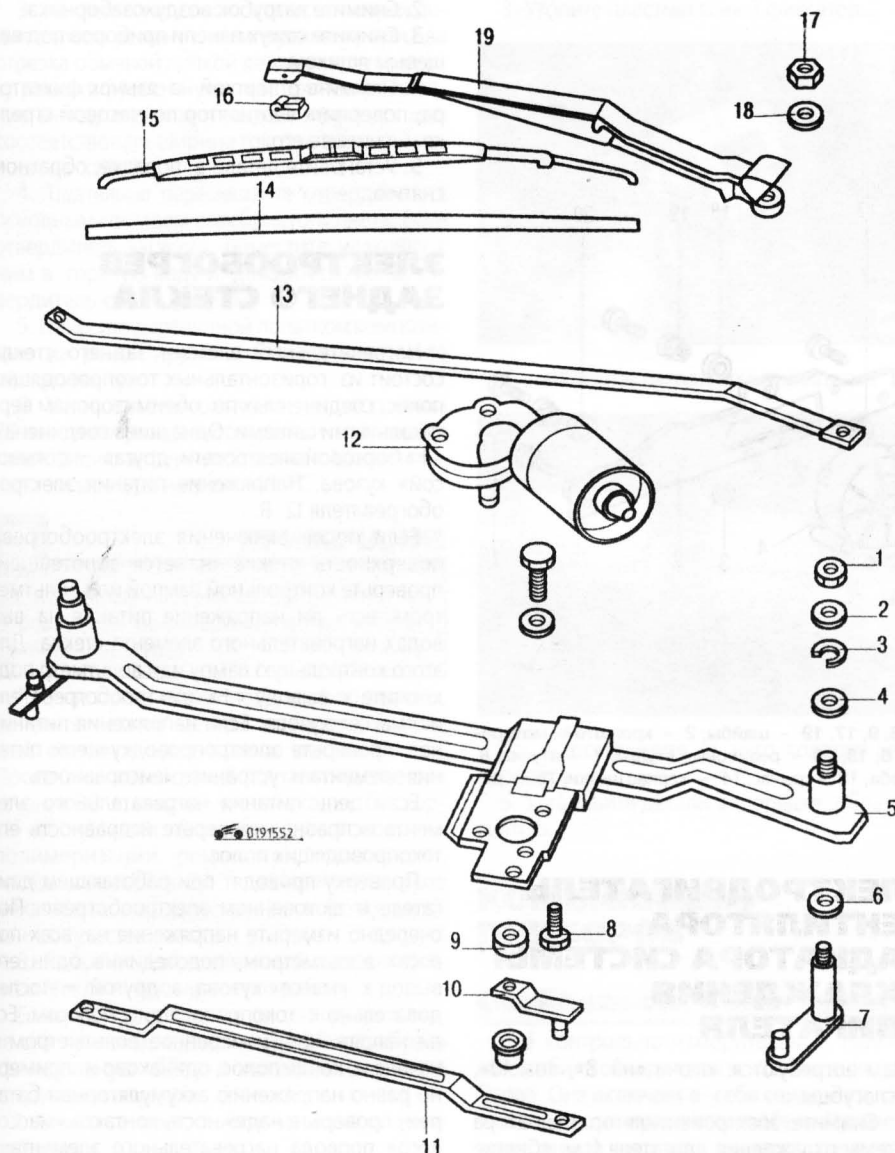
Механизм переднего стеклоочистителя: 1, 17 – гайки; 2 – пластмассовая шайба; 3 – стопорное кольцо; 4 – прокладка; 5 – кронштейн механизма стеклоочистителя; 6 – пружинная шайба; 7 – ось рычага стеклоочистителя; 8 – болт; 9 – резиновая втулка; 10 – кривошип; 11, 13 – тяги; 12 – моторедуктор; 14 – резиновый элемент щетки; 15 – каркас щетки; 16 – крепежная скоба; 18 – шайба; 19 – рычаг
